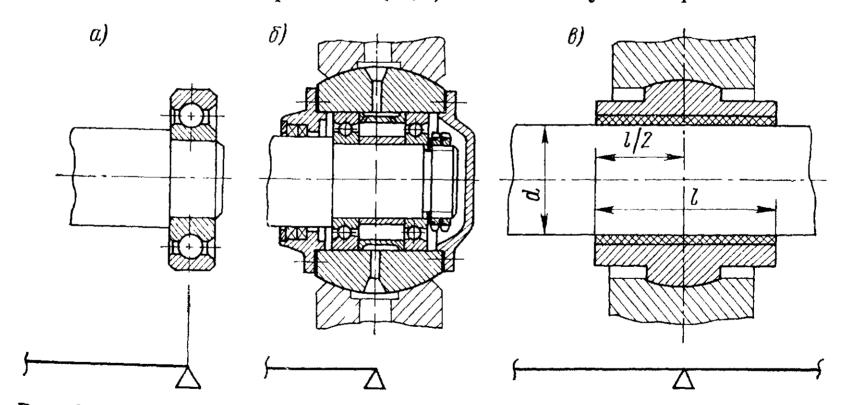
Короткие шарнирные опоры валов: a — одиночный подшипник качения; δ — сдвоенные подшипники качения, размещенные в сферической самоустанавливающейся втулке; ϵ — самоустанавливающийся подшипник скольжения
